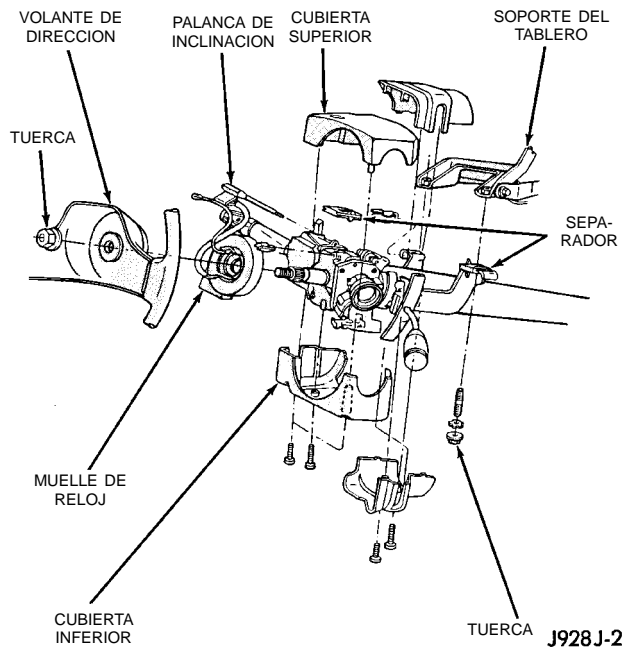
Desmontaje e instalación de las cubiertas de la columna de dirección - características
